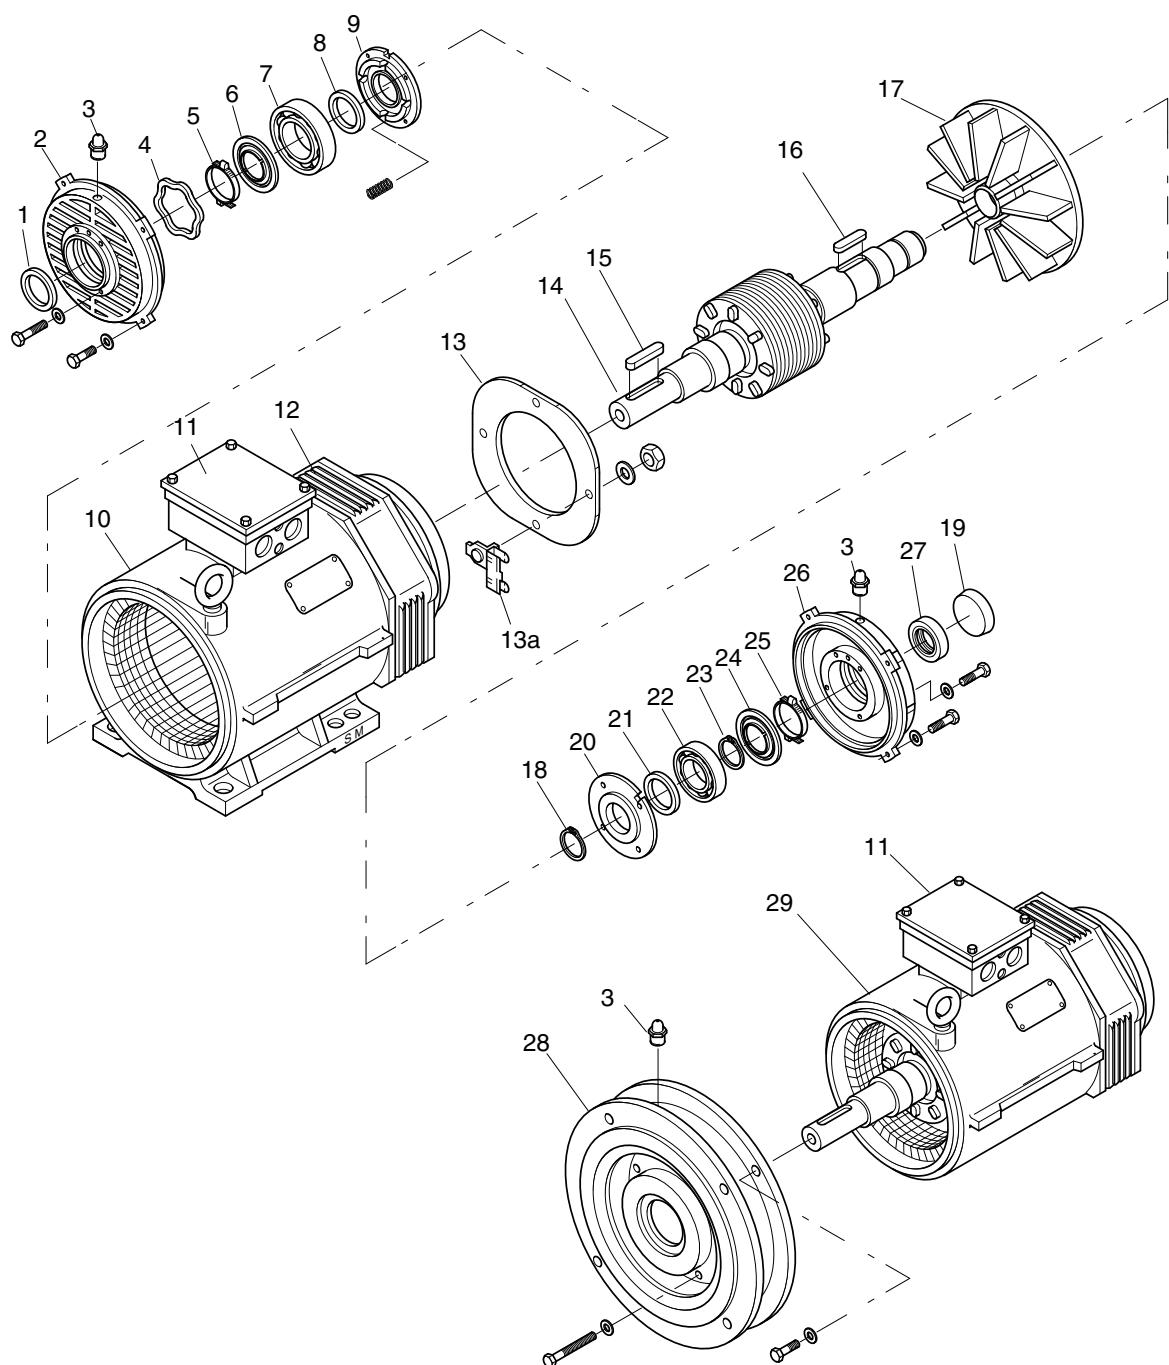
Развёрнутое изображение, IP23, типоразмер 180M-400X
